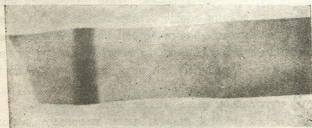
Хорошая сварка. Хороший флюс № 6.
